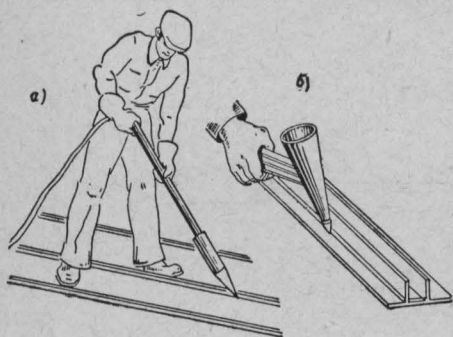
Сварка держателями: а) типа ДШ-14; б) типа ДШ-15
